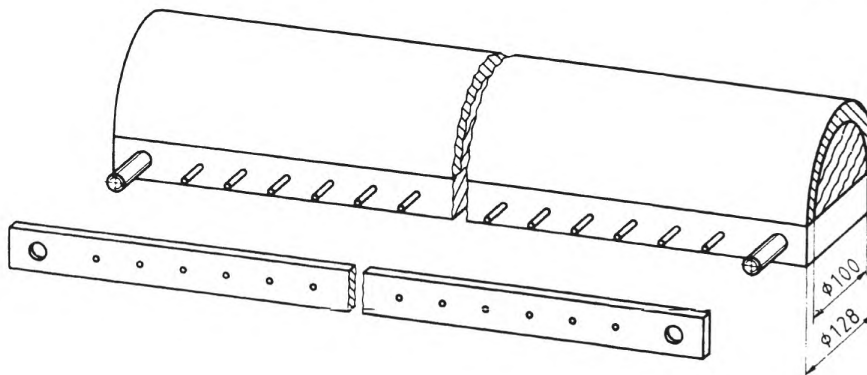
Пример опоры калибровочной подкладки и крепежного устройства
